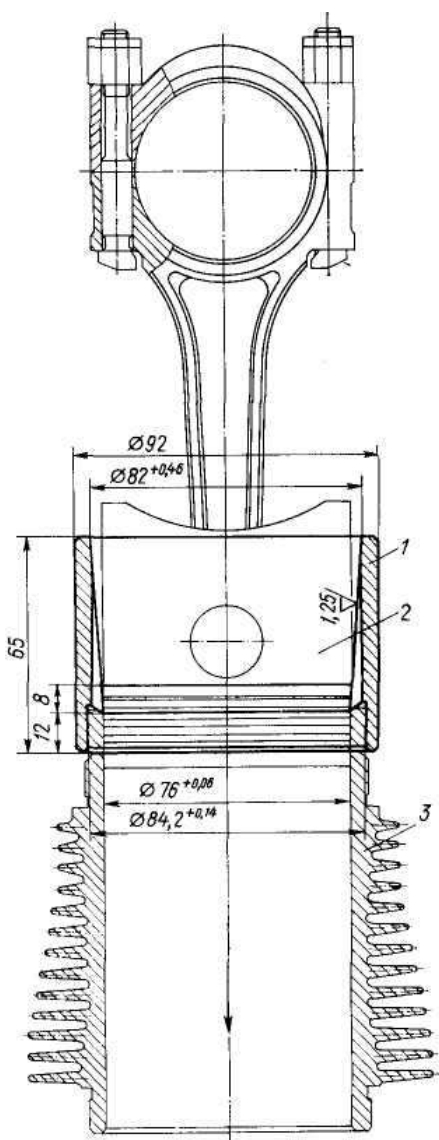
Оправка для установки поршня с кольцами в цилиндр:
